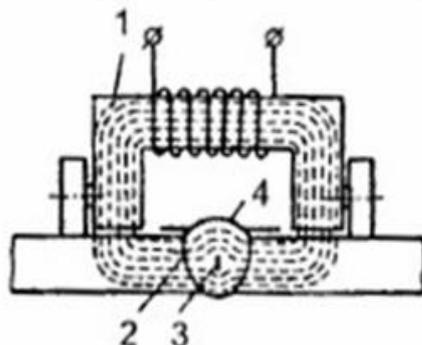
Проверка качества сварных швов магнитографической дефектоскопией: 1 - магнит, 2 - сварной шов, 3 - дефект, 4 - магнитная пленка.
